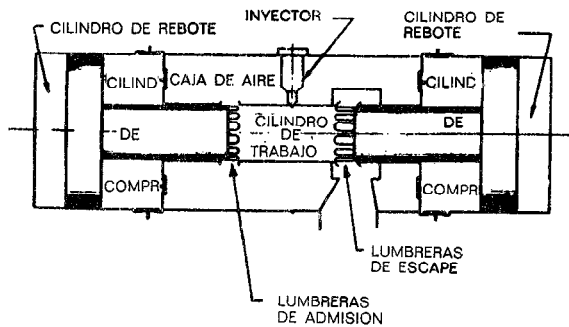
Esquema de un motor compresor de pistón libre.
